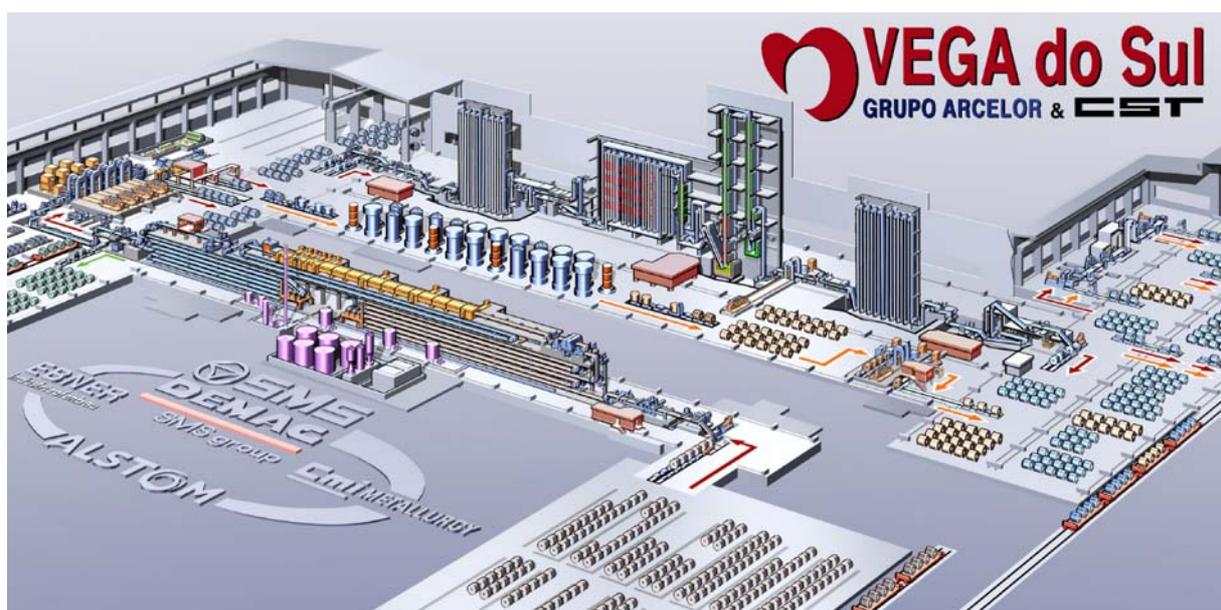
Esquemático da planta da Laminação a Frio da Vega do Sul-Arcelor Brasil
